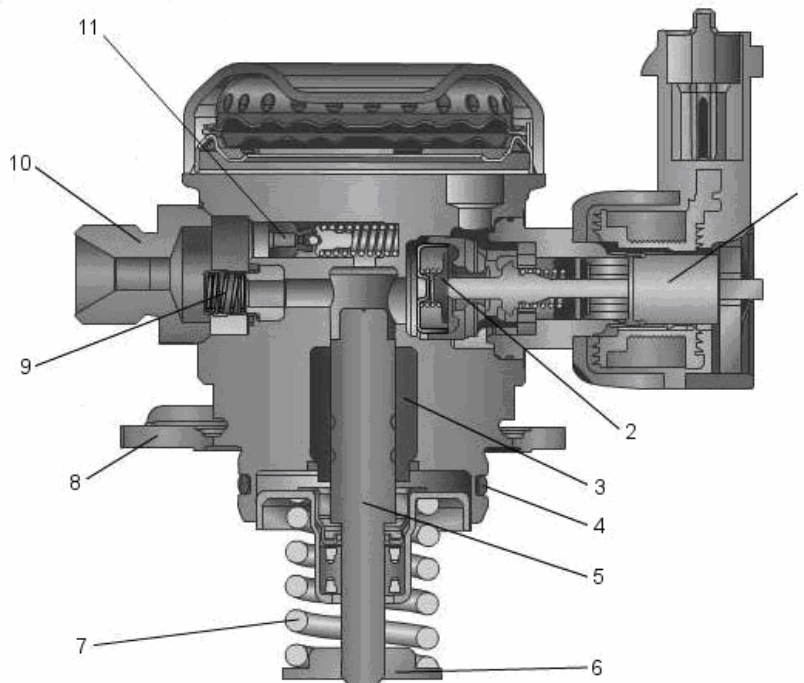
Pompa de injecție cu piston: 1- armătura mobilă; 2- supapă admisie; 3- cilindru; 4- inel etanșare; 5- piston; 6- suport arc; 7- arc; 8- flanșă fixare; 9- supapă evacuare; 10- racord rampă combustibil; 11- supapă suprapresiune
